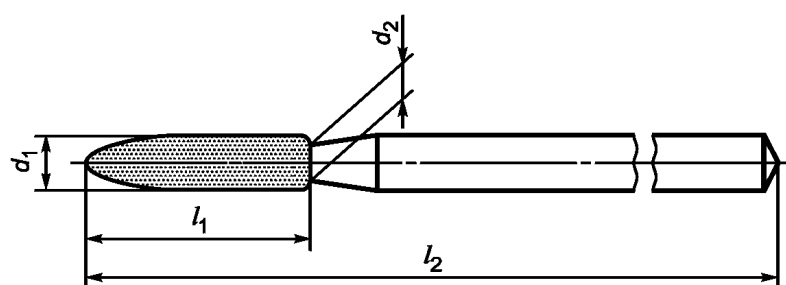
Цилиндрическая с огивальным концом рабочая часть с длиной головки 8,0 мм
